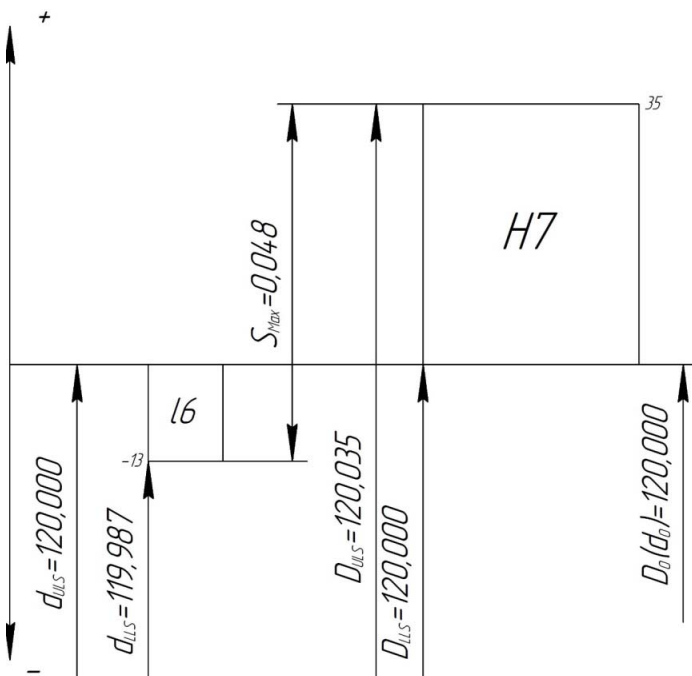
Схема расположения полей допусков размеров деталей, образующих сопряжение $\varnothing 120 \frac{H7}{h6}$
